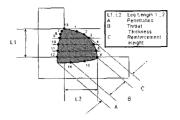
용접 형상 정의 Fig. 2 The parameters defining the weld bead shape
